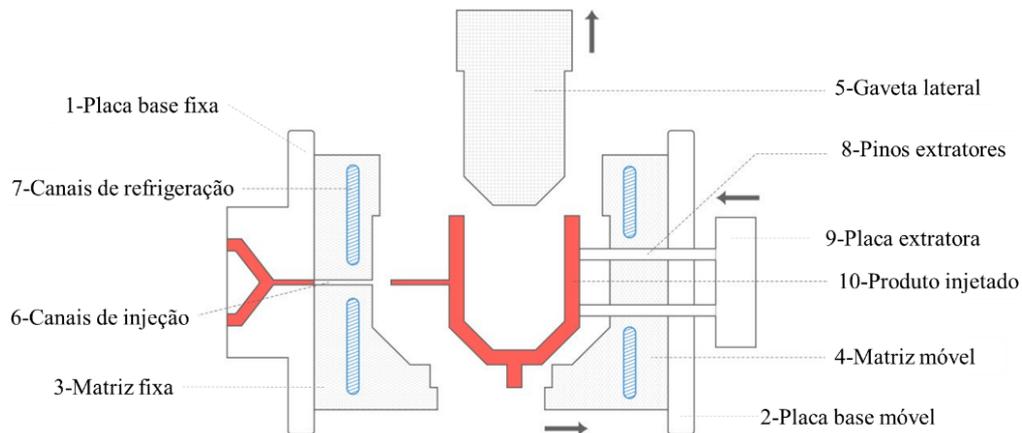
Representação esquemática de um molde de injeção com partes móveis
